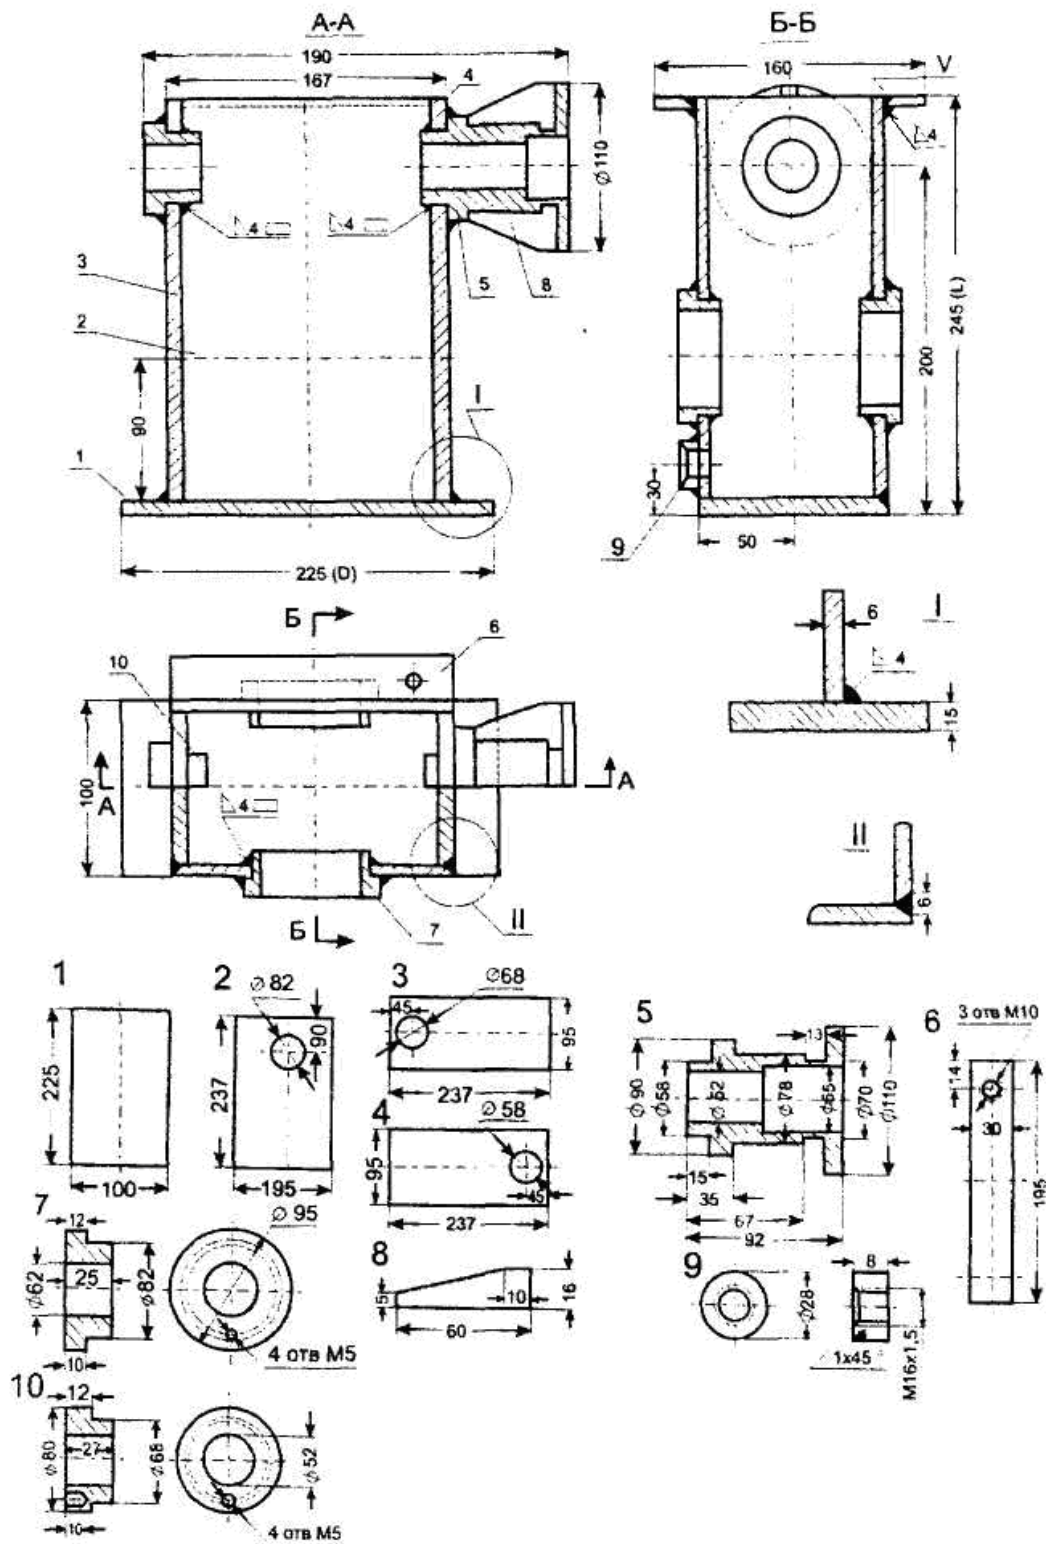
Эскизы корпуса редуктора и деталей к нему для задания № 10
